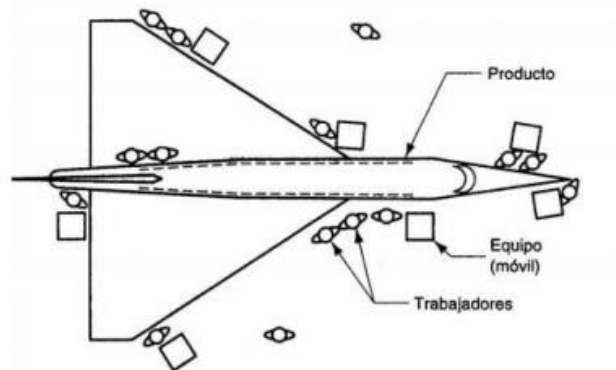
Ejemplo de distribución fija: construcción de avión
